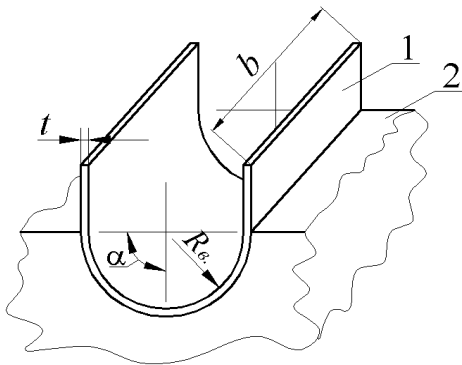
Схематичне зображення U- подібної заготовки з ідеально пластичного матеріалу, отриманої гнуттям у штампі: 1 - заготовка, 2 - нижня напівматриця
